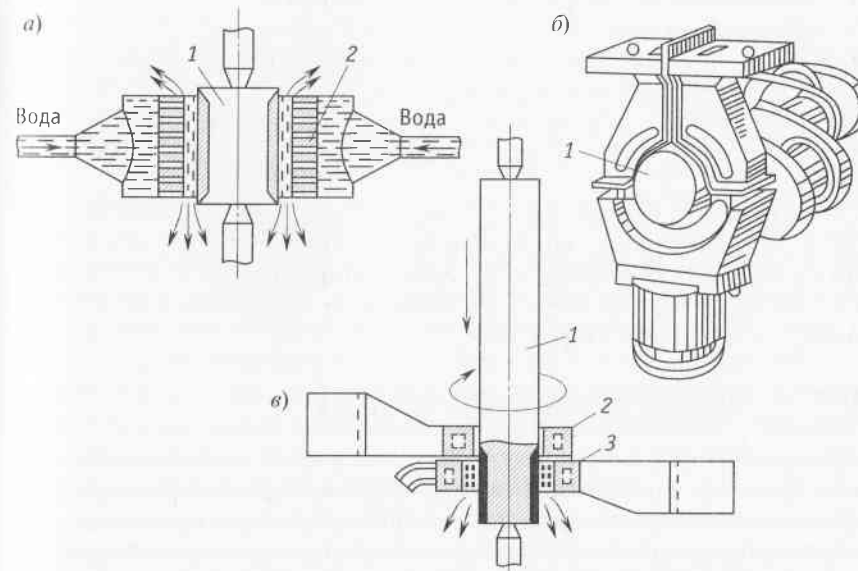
Поверхностная закалка деталей токами высокой частоты: а — одновременный нагрев и охлаждение; б — непрерывно-последовательный нагрев вдоль оси вала; в — последовательный нагрев и охлаждение каждой шейки коленчатого вала
